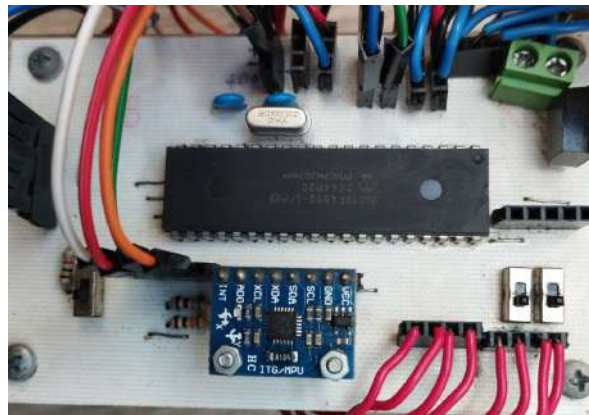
Vista superior de tarjeta PCB colocada en el robot balancín.
